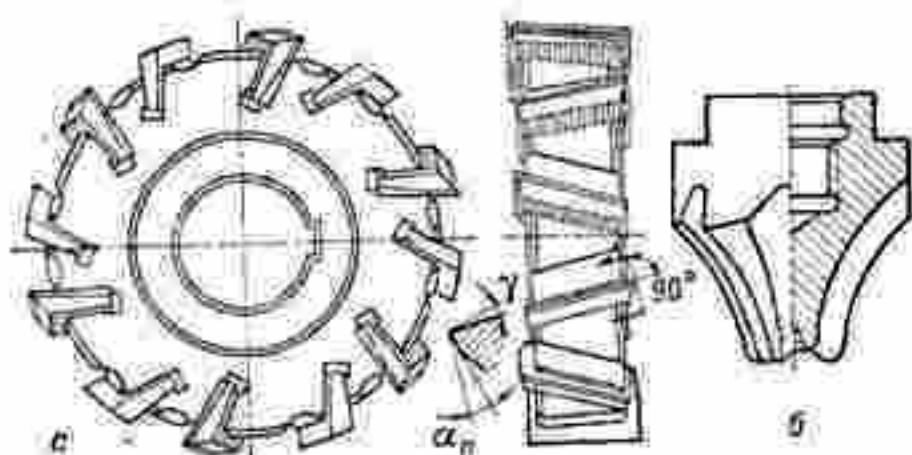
Зуборезные фрезы: а — дисковая; б — пальцевая; a_n — задний угол зуба фрезы и плоскости, перпендикулярной оси фрезы; γ — передний угол.
